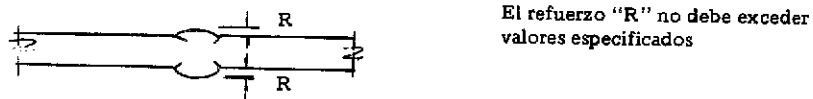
Líneas de fuerza en las uniones soldadas.
